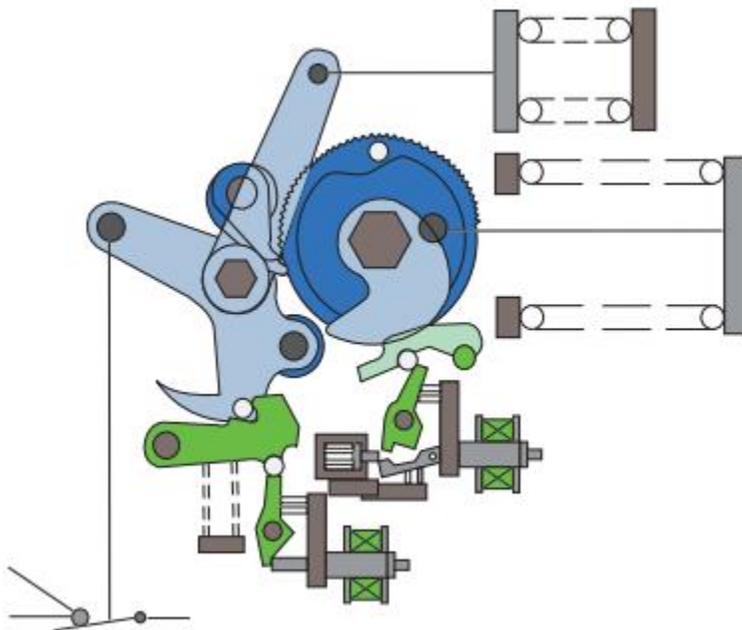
Posición cerrada (resorte de cierre sin carga).
